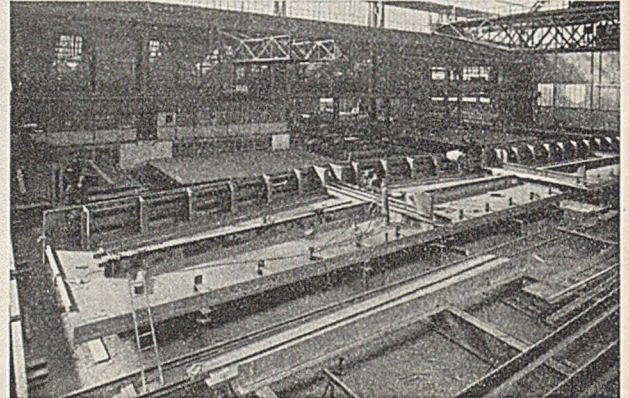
Arbeitsplatz 3. Die Seitenwände werden weiter um 90° gedreht und die Kehlnähte auf der Innenseite zwischen Gurt und Stegblech gelegt, die Längsaussteifungen und Querträgeranschlüsse angebaut und verschweißt.
